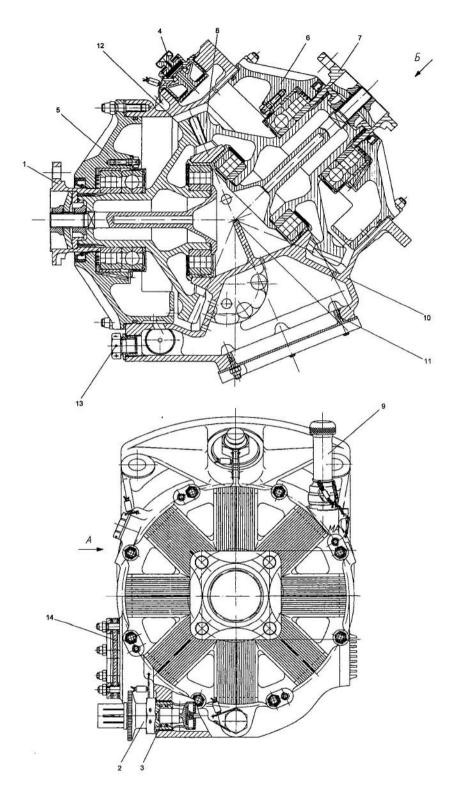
(Лист 1 из 3) Редуктор промежуточный
